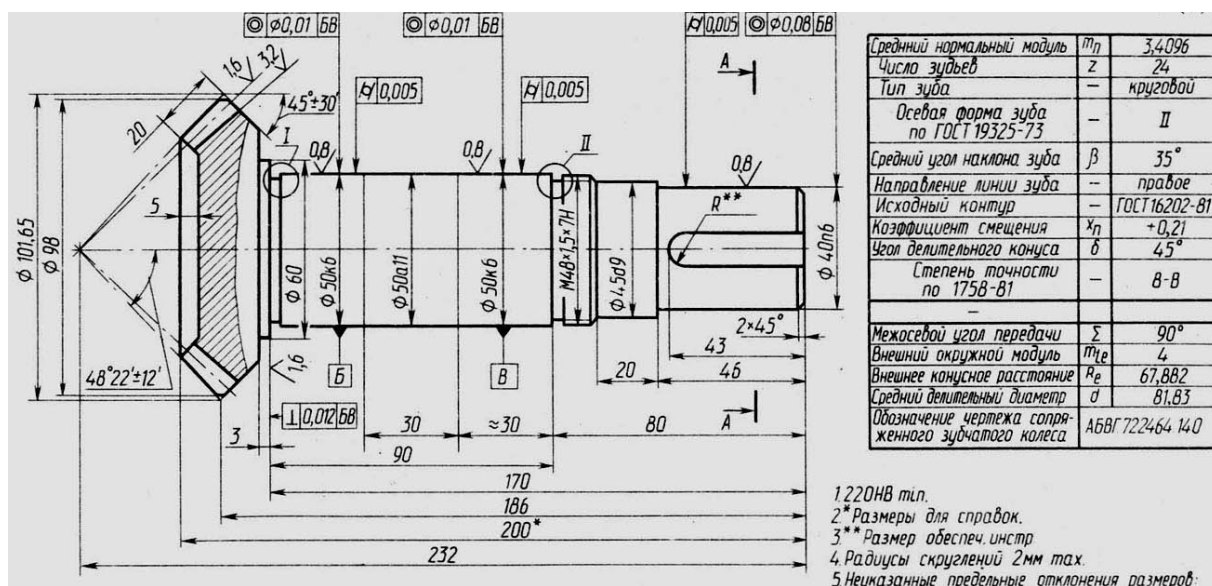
Робоче креслення деталі “вал-шестерня”
